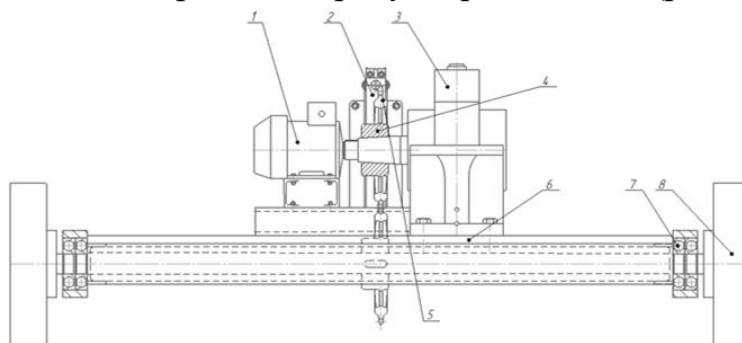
Механизм передвижения крана: 1 – электродвигатель; 2 – тормоз; 3 –редуктор; 4 –звездочка приводная; 5 – цепь; 6 – рама; 7 –подшипник; 8 – мост.
